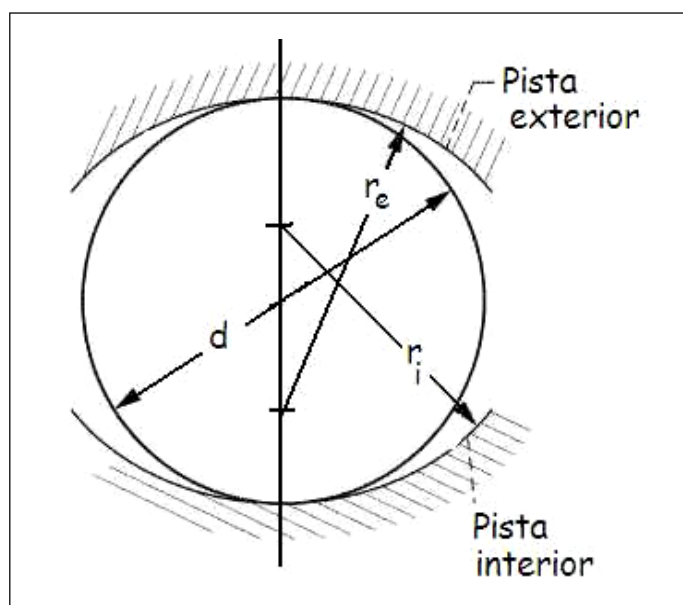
Contacto del elemento rodante tipo bola con las pistas de los aros exterior e interior de un rodamiento.
